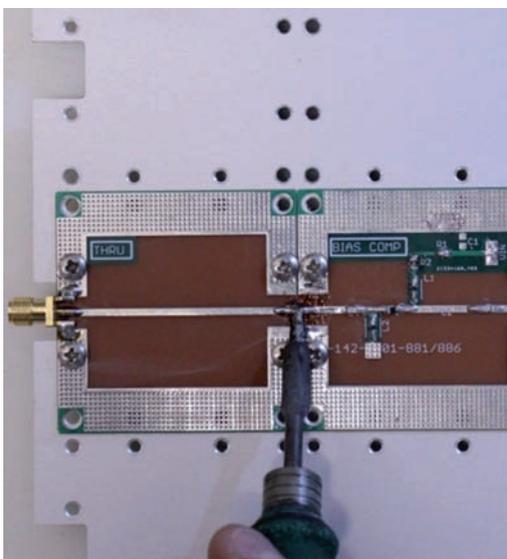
bis - Saldatura fra le piste di moduli adiacenti
